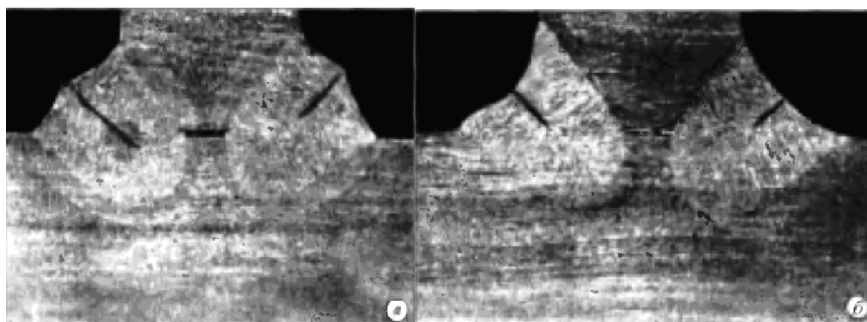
Продольные и поперечные трещины (слева); расположение трещин по сечению шва при электрошлаковой сварке:
